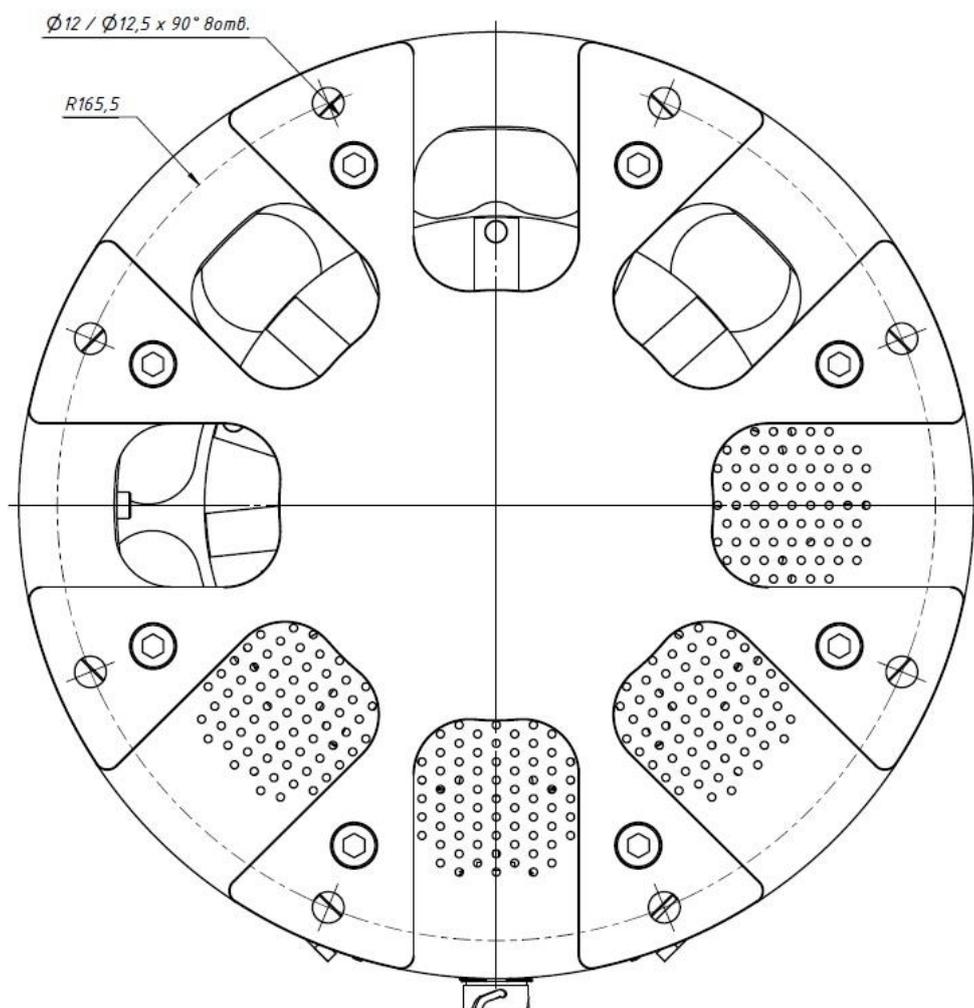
Присоединительные размеры опорно-поворотного устройства (вид снизу)
